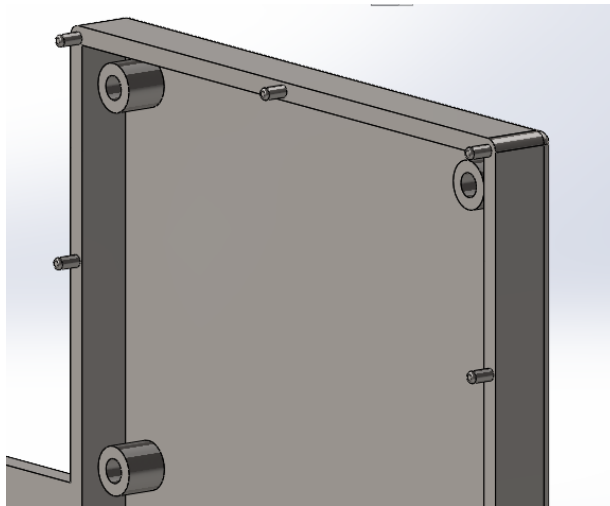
Збільшена частина деталі основи корпусу.
